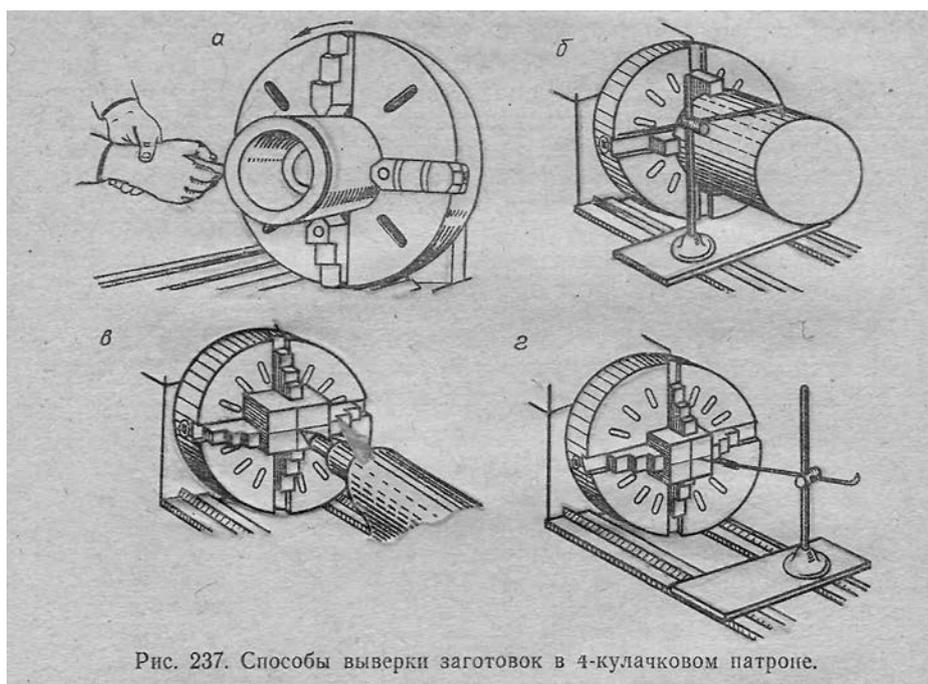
Способы выверки заготовок в 4-кулачковом патроне.
